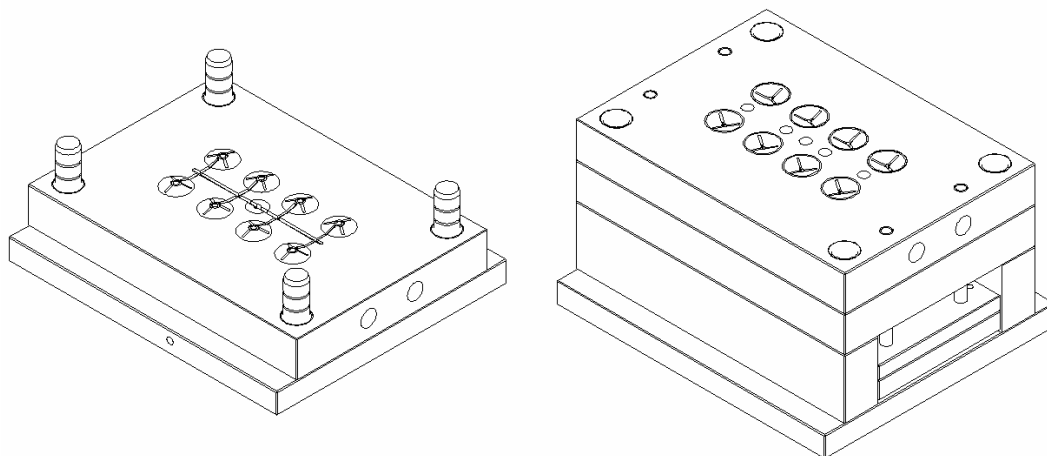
Molde para injetar a unidade representativa do carbono-alfa: vista isométrica em escala reduzida mostrando as duas partes do mesmo molde
